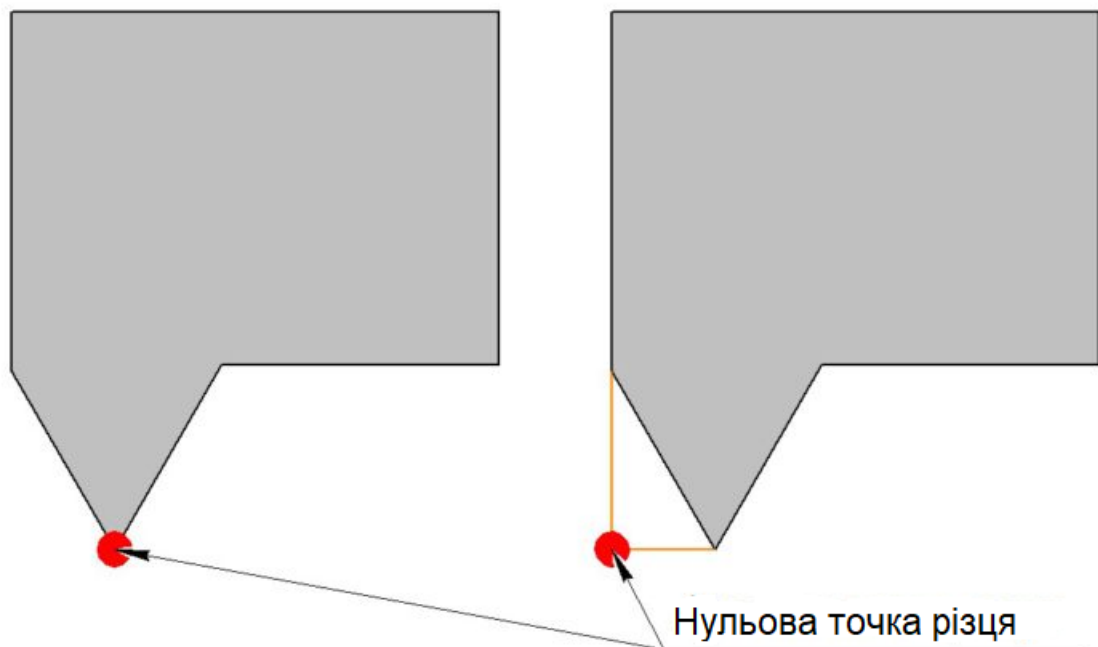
Варіанти розташування нульової точки інструмента
